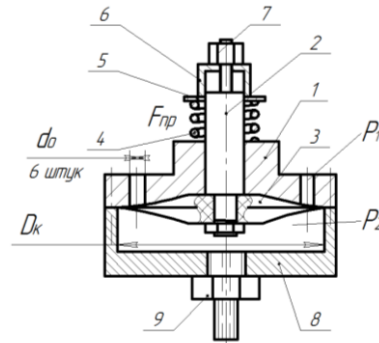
Розрахункова схема зворотного клапану вібраційної машини для очистки забруднень потоком пульсуючого струменя рідини з твердими частинками: 1 – корпус; 2 – шток; 3 – пружина мембрана; 4 – пружина; 5 – шайба; 6 – стакан; 7 – гайка регульовальна; 8 – кришка; 9 – штуцер
